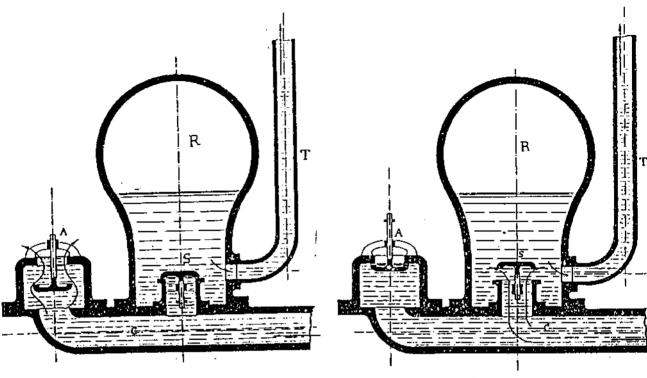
Coupe d'un bélier. Période de refondement. Soupape d'arrêt fermée.
